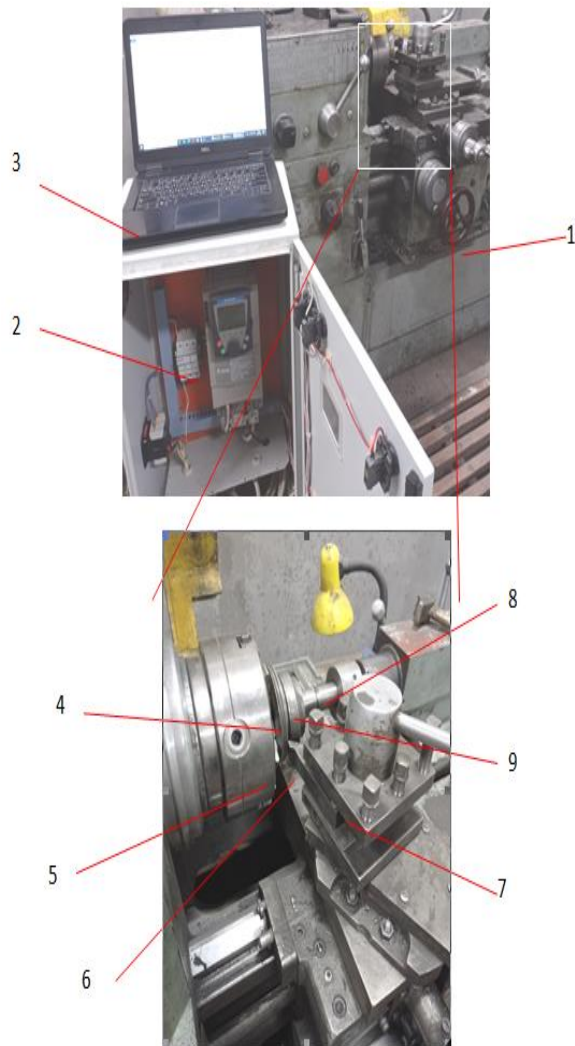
Процес проточування витків заготовки гвинтового секційного робочого органу на токарно-гвинторізному верстаті: 1 – токарно-гвинторізний верстат; 2 – частотний перетворювач Altivar; 3 – комп’ютер; 4 – заготовка гвинтового секційного робочого органу із стиснутими витками; 5 – трьохкулачковий патрон; 6 – прохідний різець; 7 – різетримач; 8 – задній центр; 9 – затискна шайба
